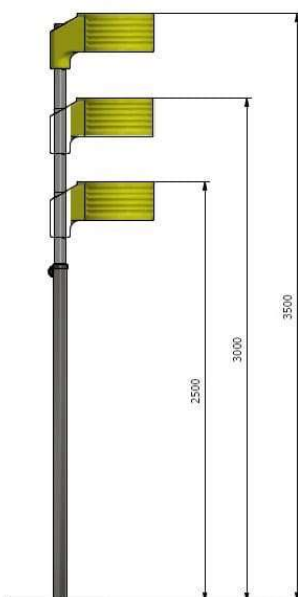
Przykładowy schemat montażu kosza do streetball
